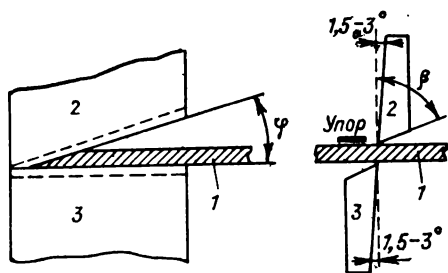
Схема механической резки металла на гильотинных ножницах.
